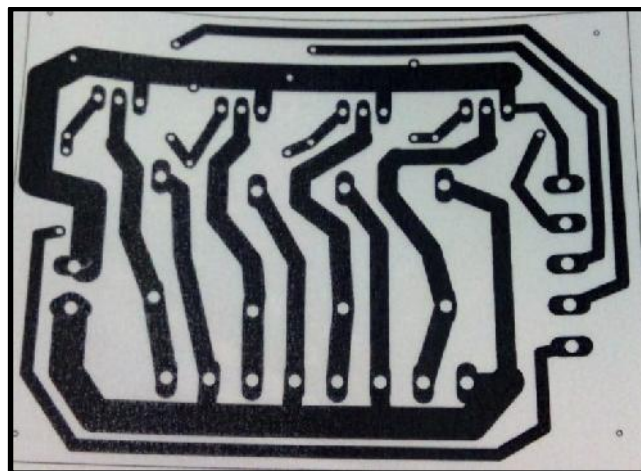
Cara soldadura impresa en papel vegetal
